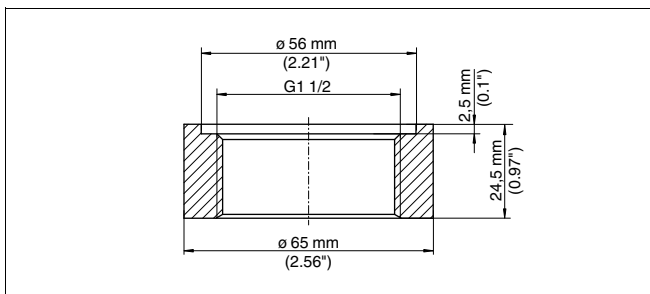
Размеры приварного штуцера G1½ A по DIN 3852-X
